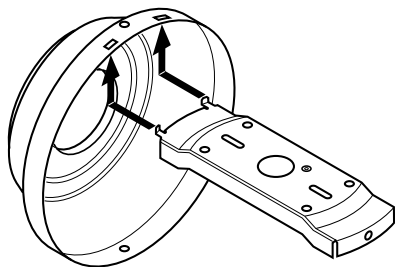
Installation des crochets dans la plaque de plafond sur les fentes dans le pavillon
